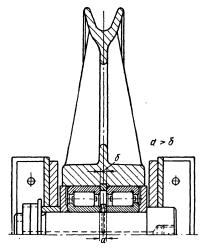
Канатный шкив на радиальных роликоподшипниках с цилиндрическими роликами
